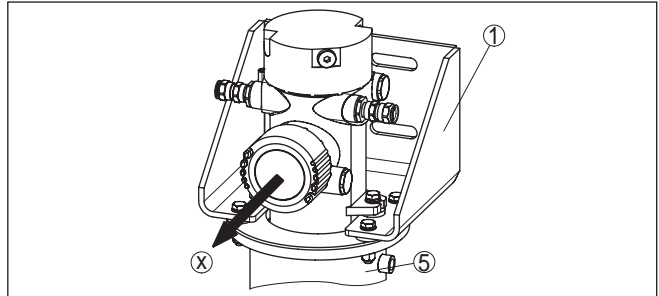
Montagerichtung des Sensors zum Befestigungswinkel
